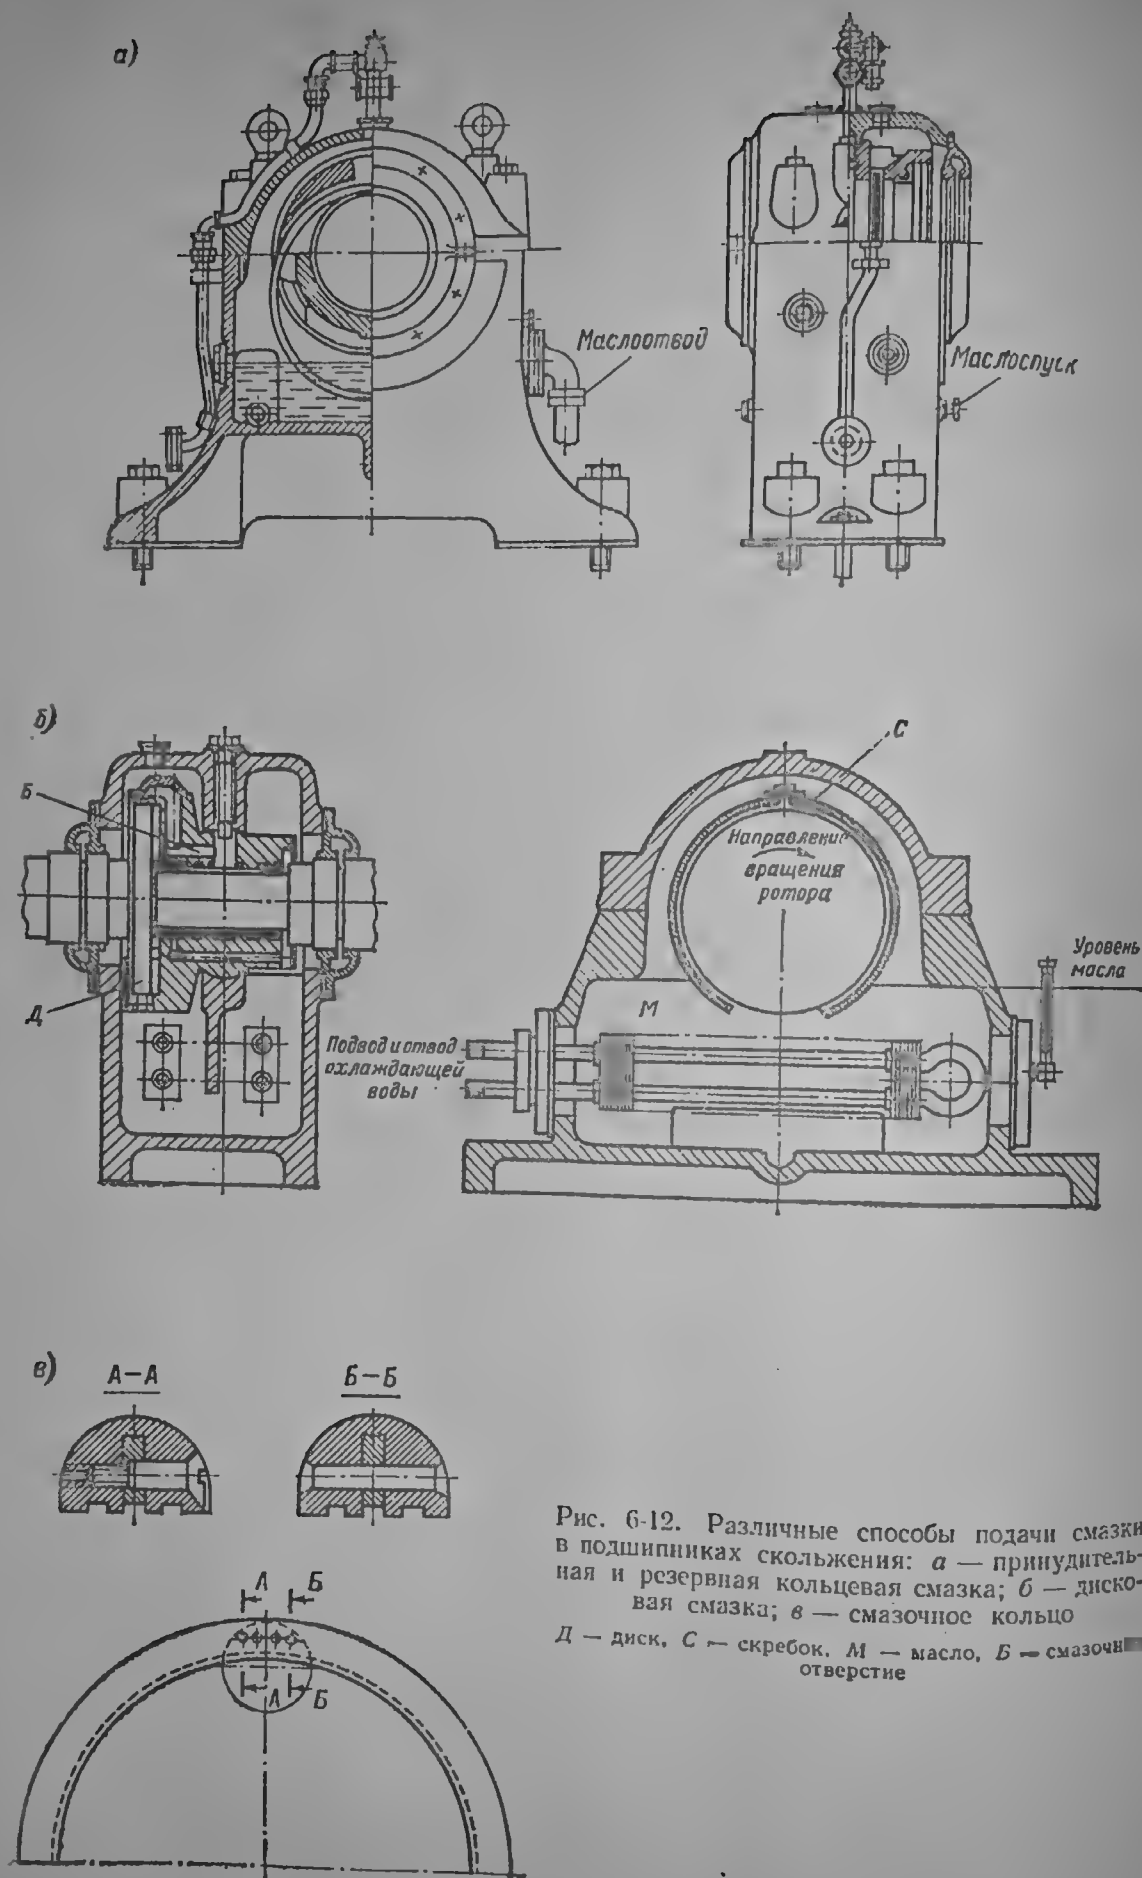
Различные способы подачи смазки в подшипниках скольжения: а — принудительная и резервная кольцевая смазка; б — дисковая смазка; в — смазочное кольцо; г — диск, С — скребок, М — масло, Б — смазочное отверстие
